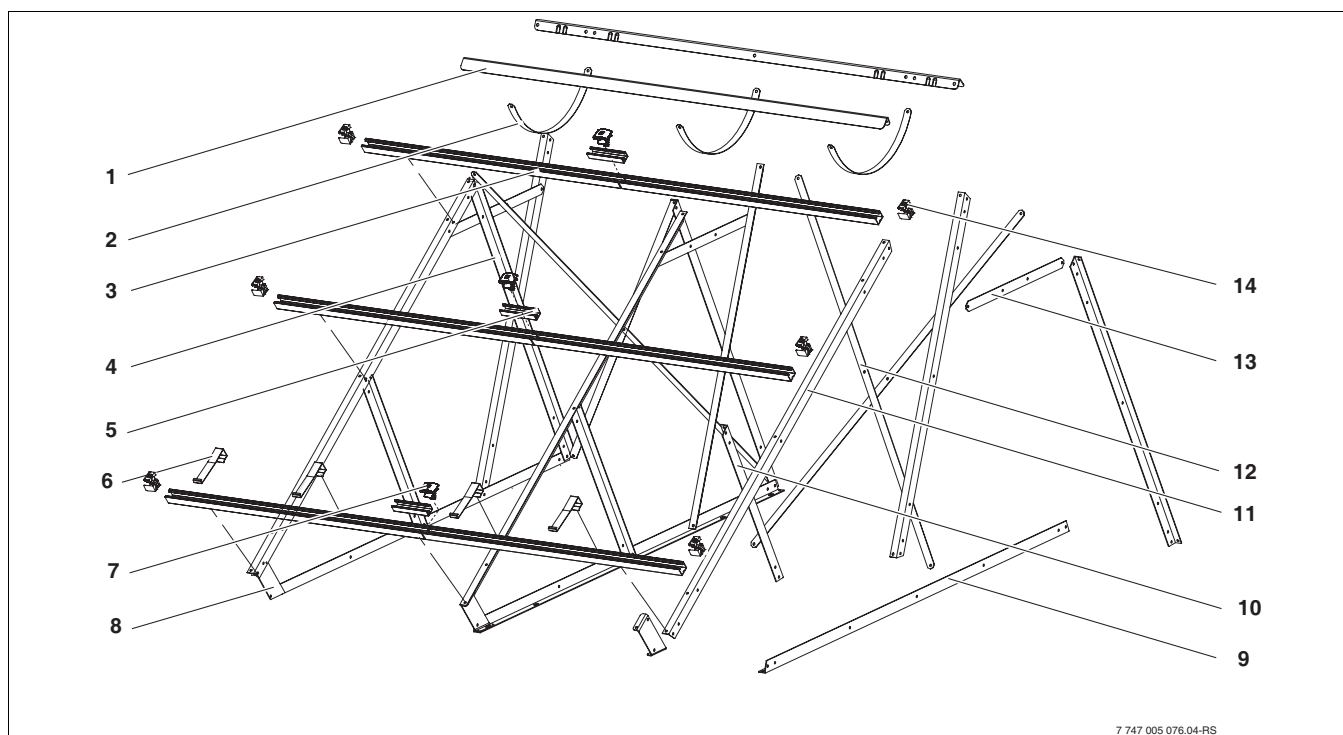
Juegos de montaje para 2 captadores: 1 juego de soporte básico, 1 juego de soporte adicional
